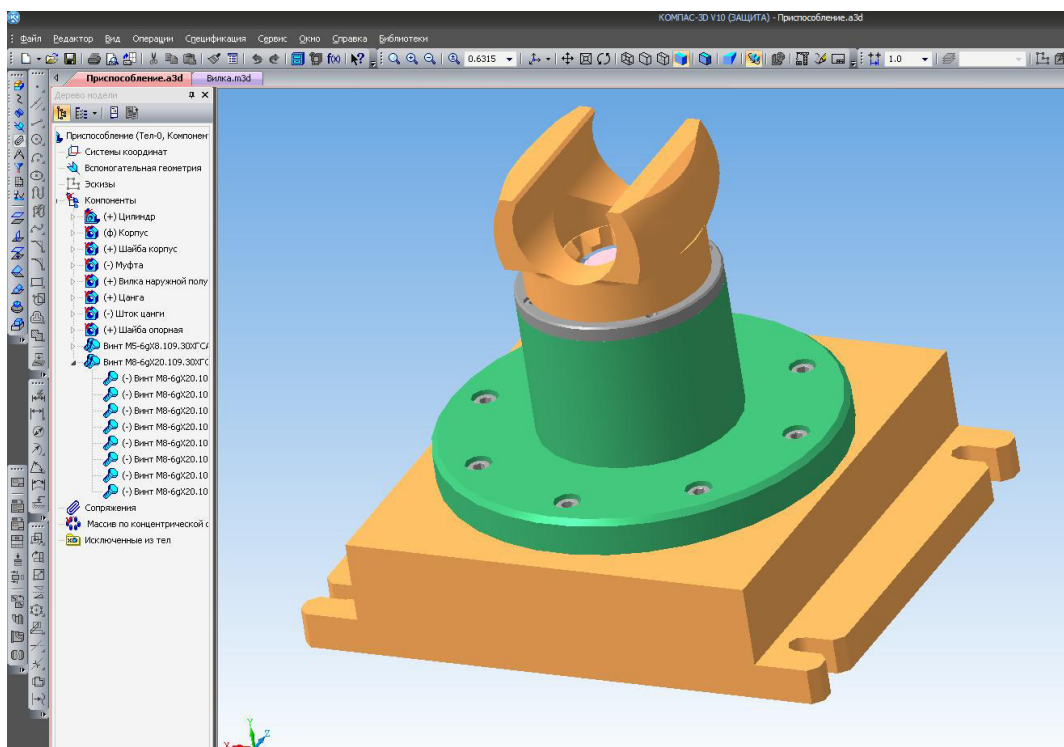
3D модель станочного приспособления для комплексной обработки
